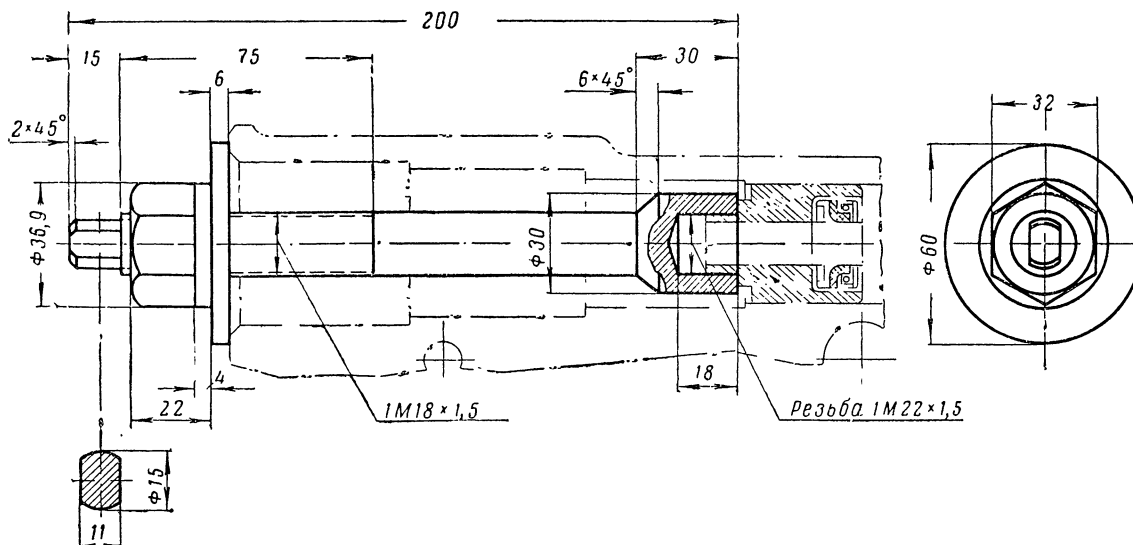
Приспособление для выпрессовки направляющей втулки толкателя сервомеханизма.
